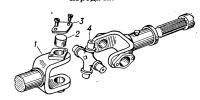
Полный кардан? 1 — вилка; - опора для цапф крестовины; 3 — крышка; 4 — крестовина.
